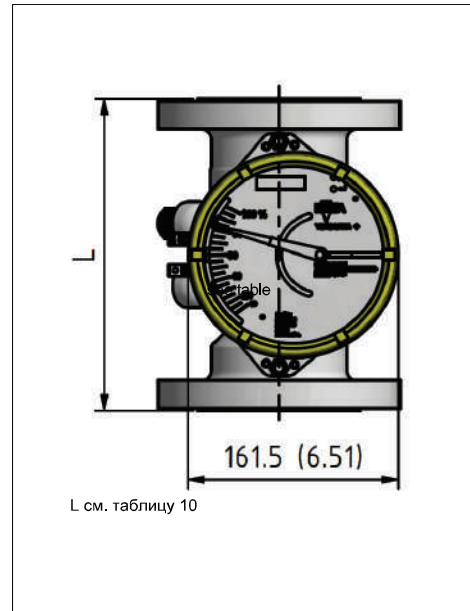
б. Корпус, тип 91 (Al), вид спереди, размеры в мм (дюймах)
